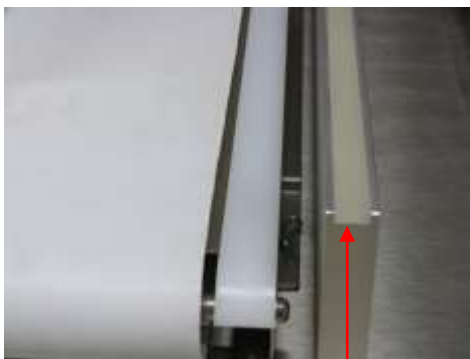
Ersetzen des Schweißdrahts
